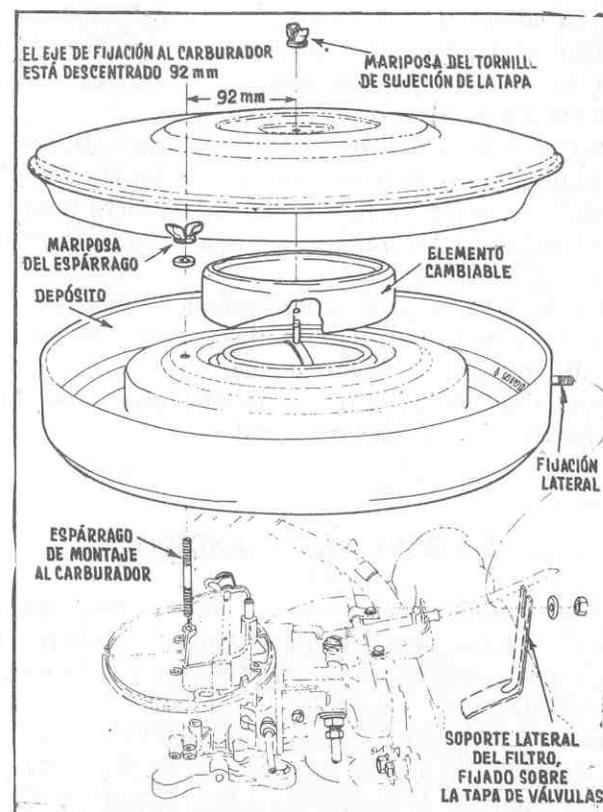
Montaje del filtro de aire en el motor 221 SP.
